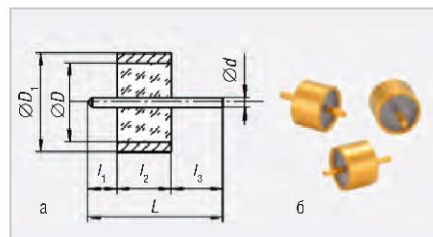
Конструкция СВЧ-ввода (а) и его внешний вид (б)
